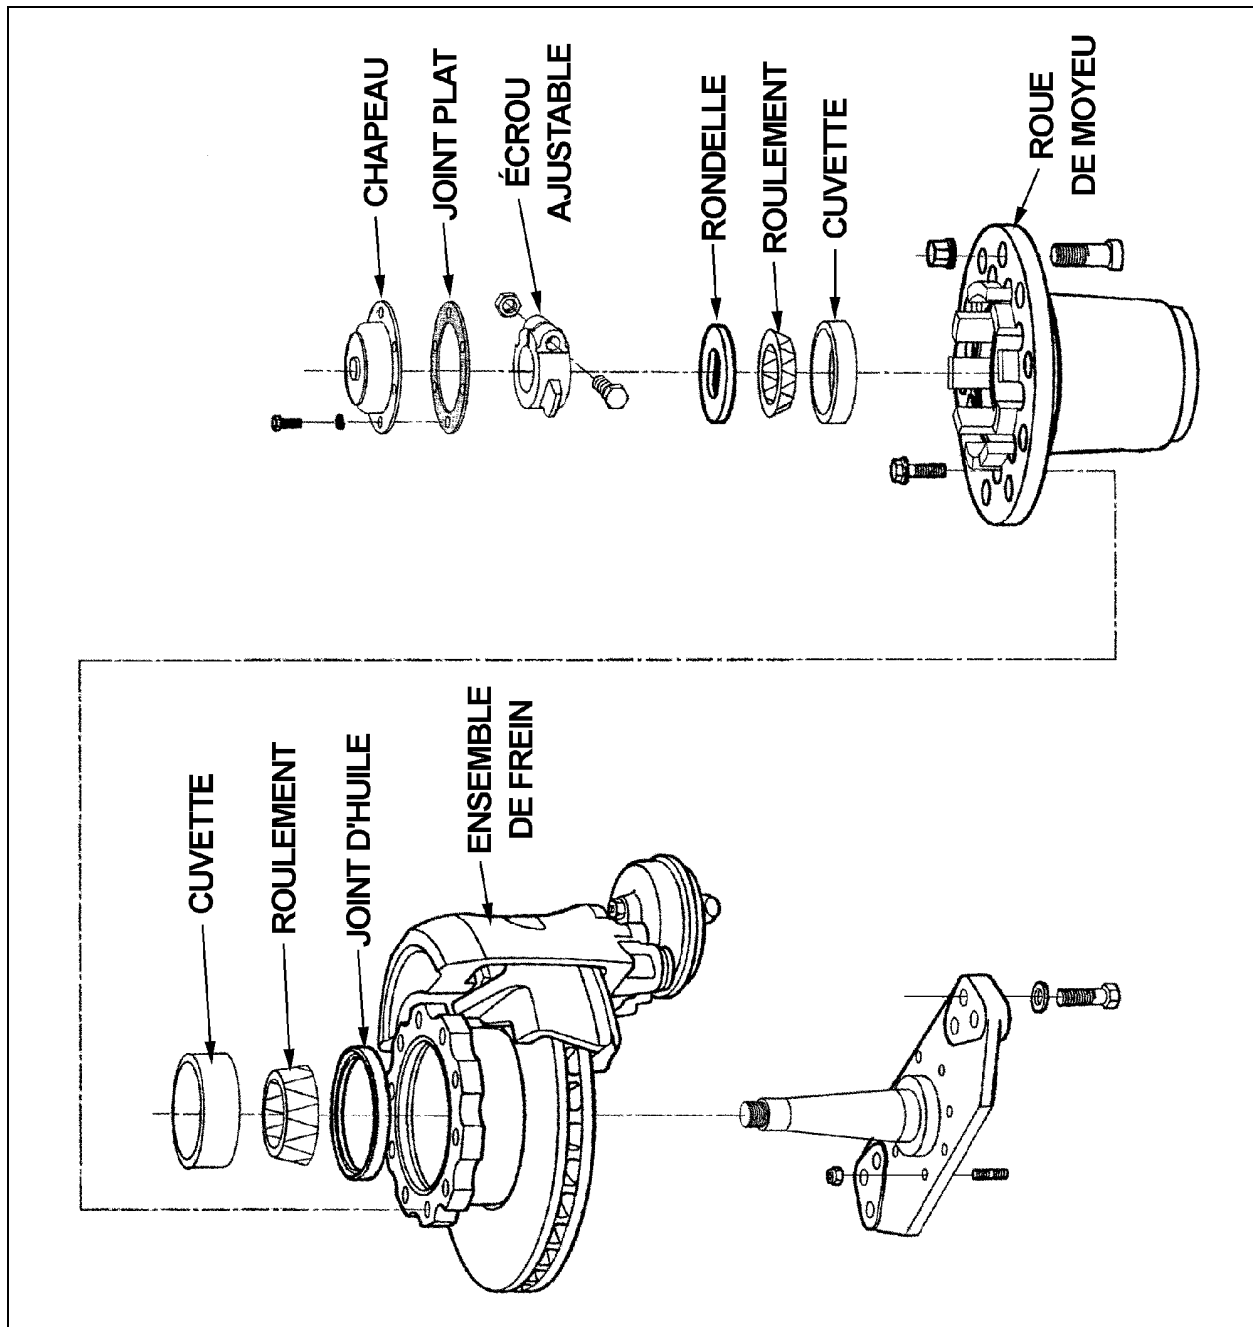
ENSEMBLE DISQUE ET MOYEU – ESSIEU PORTEUR (TYPIQUE)
